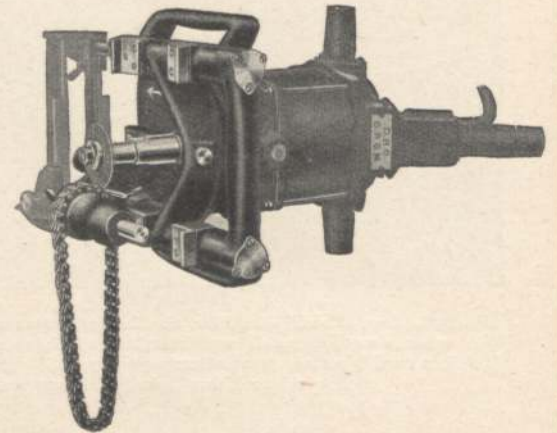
Der Schleifapparat für die zum Schmalzschken Kettenstemmapparat benützten Fräsketten.
